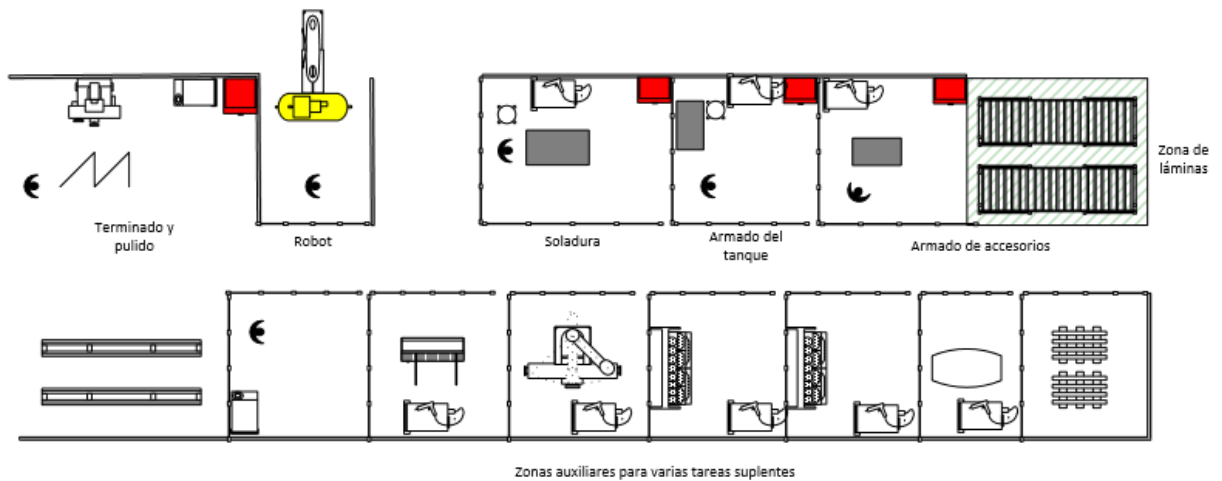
Vista superior de la planta actual (Realizada en VISIO)
